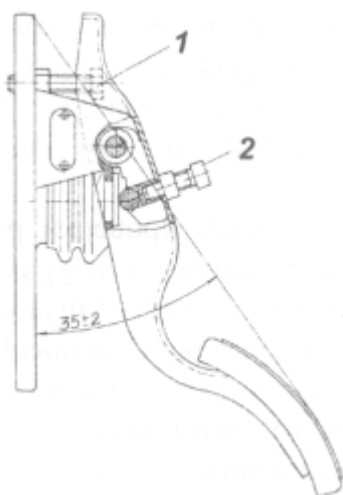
Схема установки педали на тормозной кран: 1 - установочный болт; 2 - регулировочный болт.
